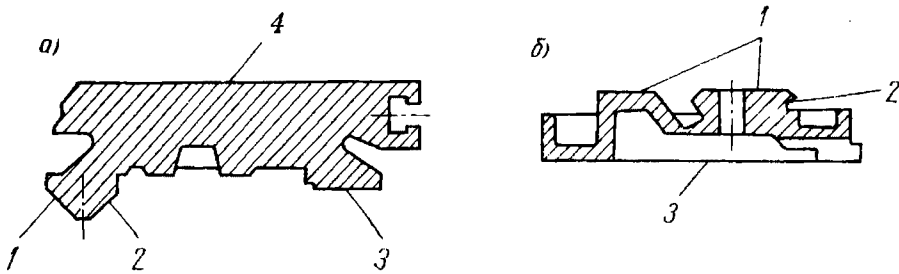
Узел стола: *а* — нижний стол; *б* — верхний стол
